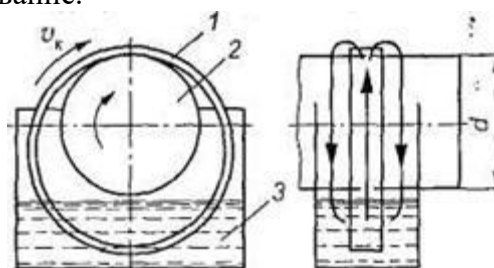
Смазывание подшипника кольцом: *1* — кольцо; *2* — цапфа; *3* — резервуар для масла
